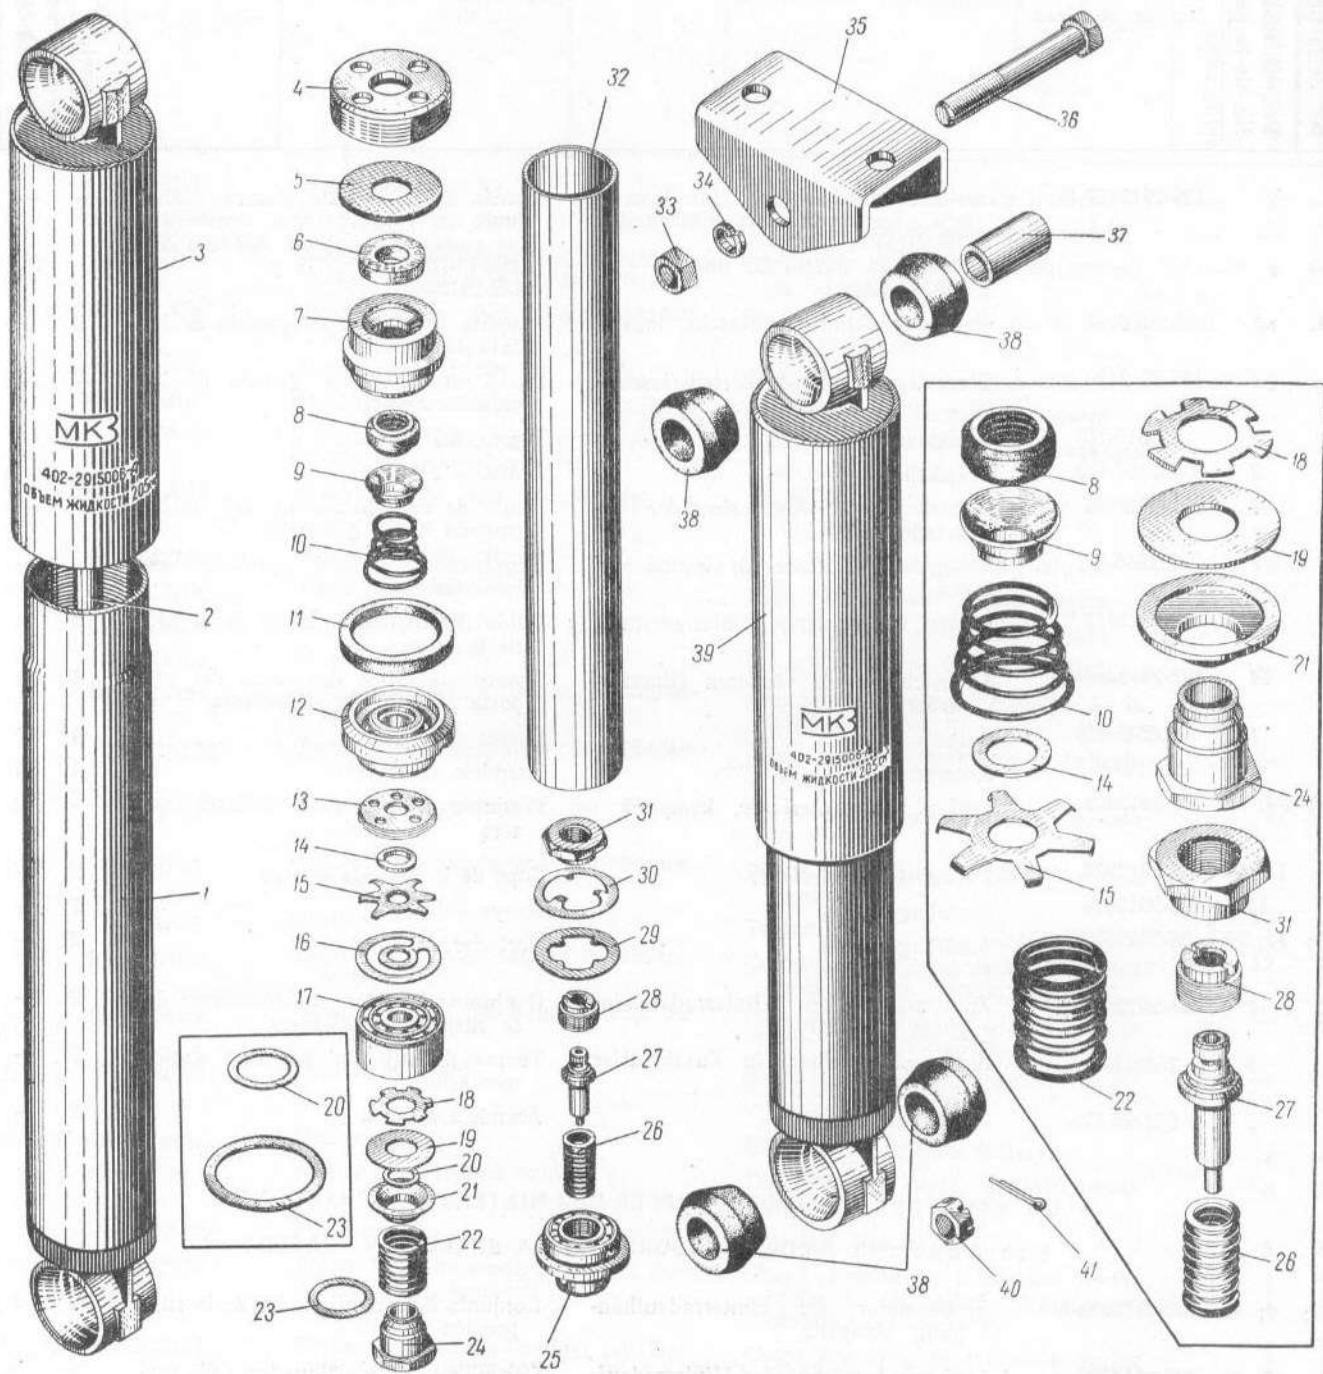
Hinterer Stoßdämpfer mit Befestigungsteilen
